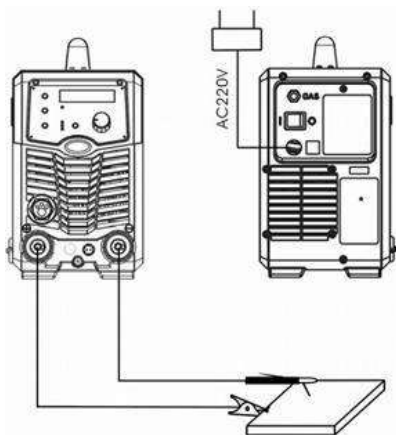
Příprava zařízení Fanmig pro svařování TIG.
